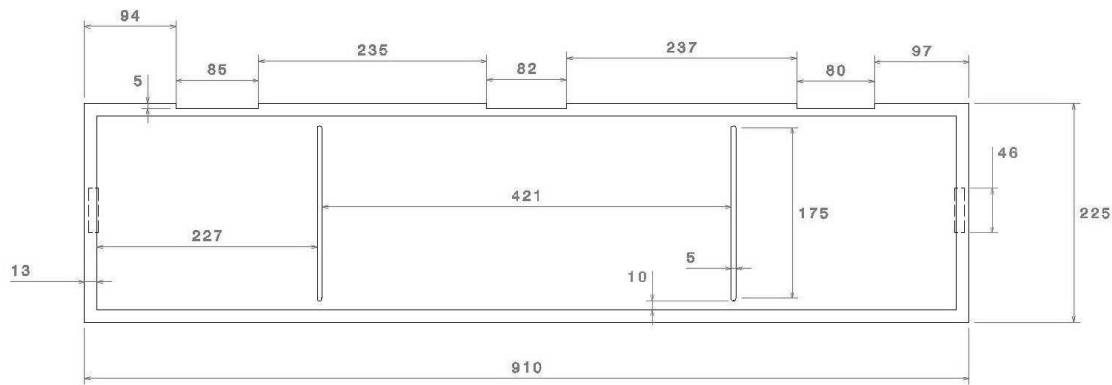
Planos de la réplica construida de la compuerta lateral del túnel de viento. Elaboración propia.
